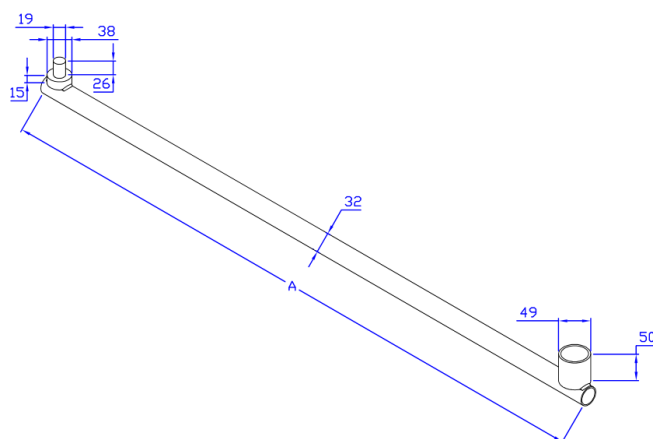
Palanca de dos brazos (puerta de salida). Anexo A Plano 6 a Plano 9
